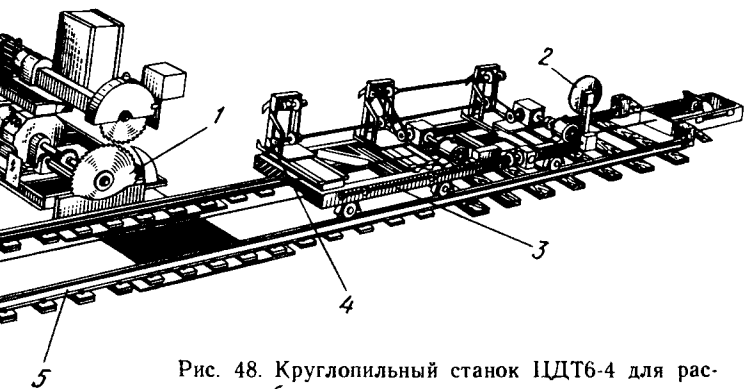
Круглопильный станок ЦДТ6-4 для распиловки бревен:
